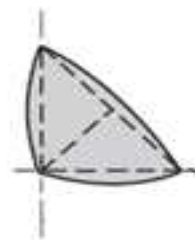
Cordón de soldadura ligeramente convexo
